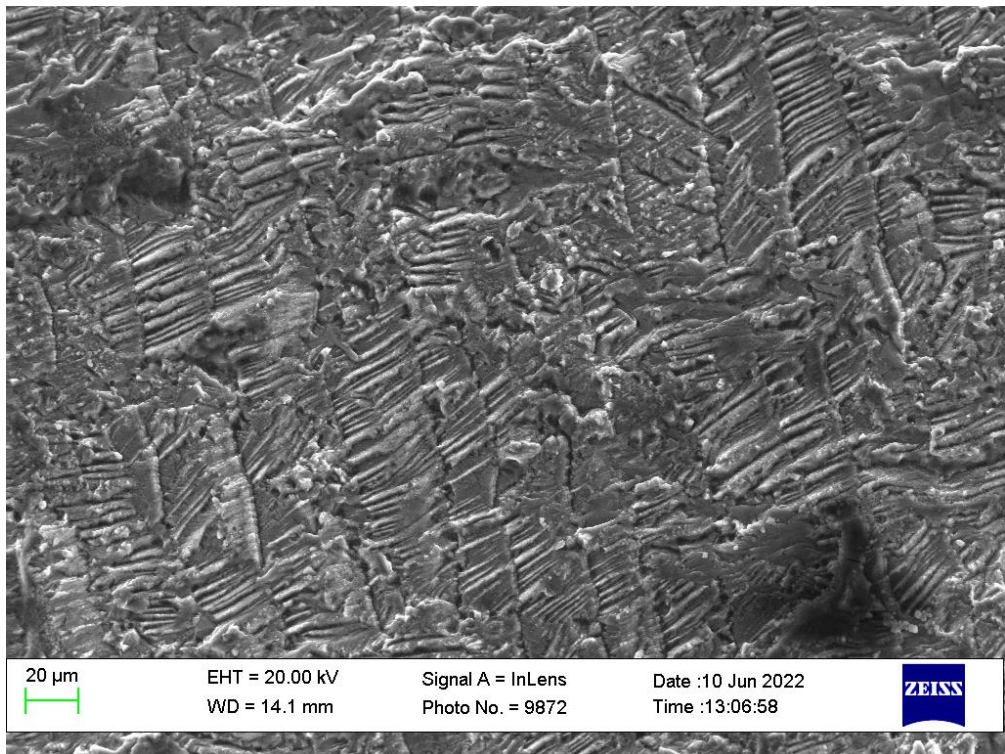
Микрорельеф поверхности излома вблизи очага разрушения.
